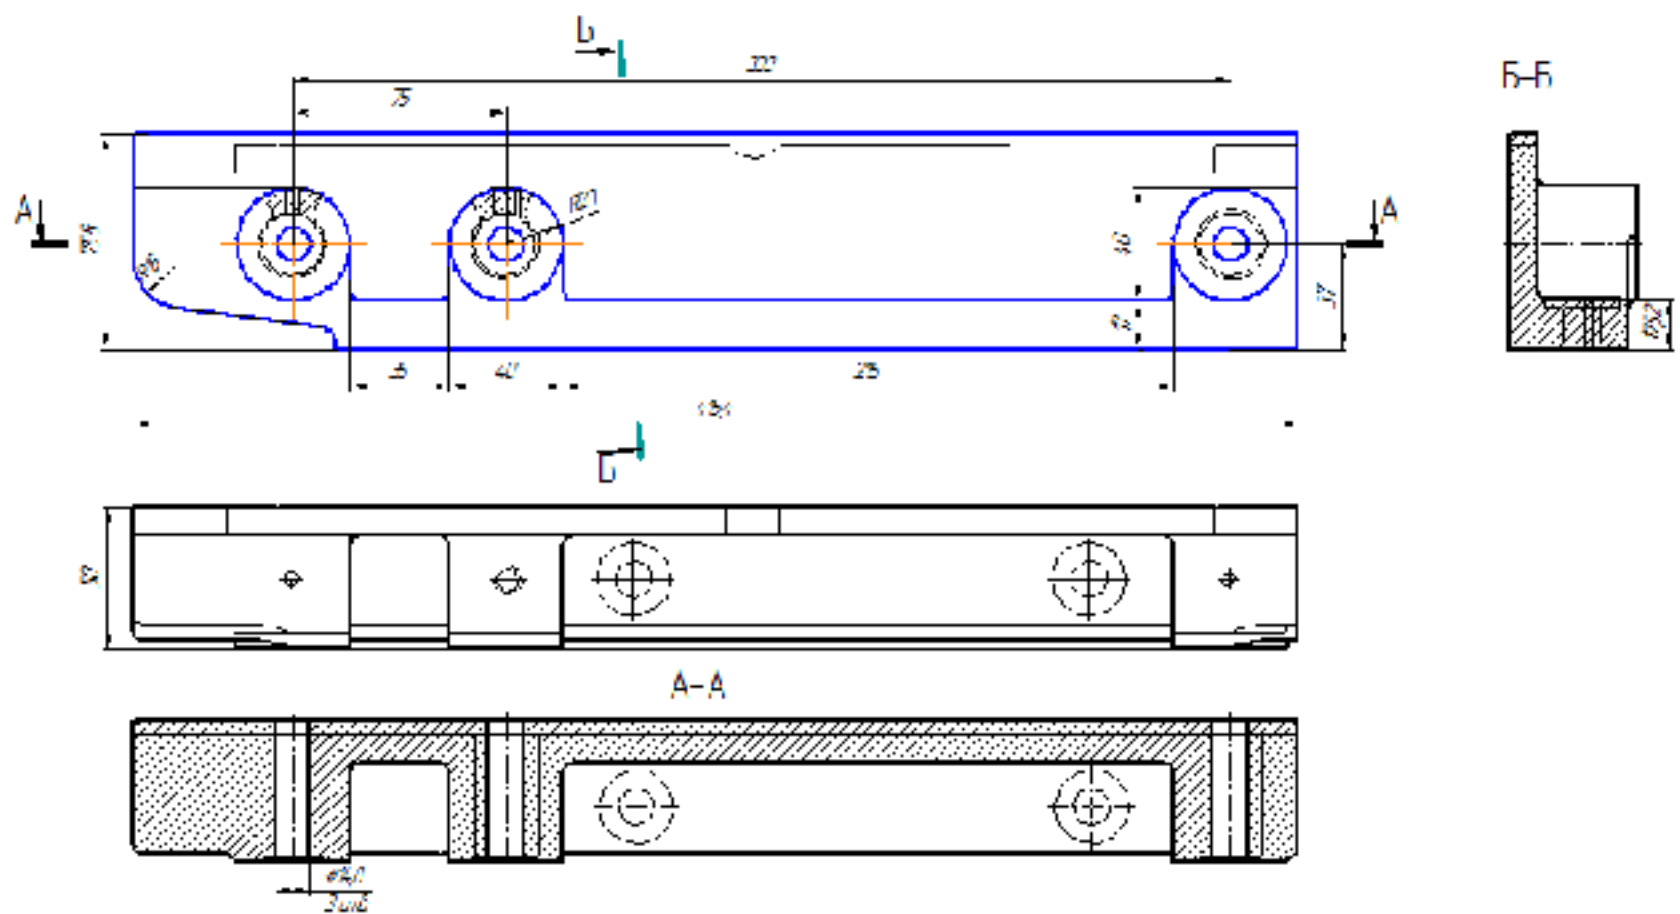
Ескіз заготовки при литті в оболонкові форми
